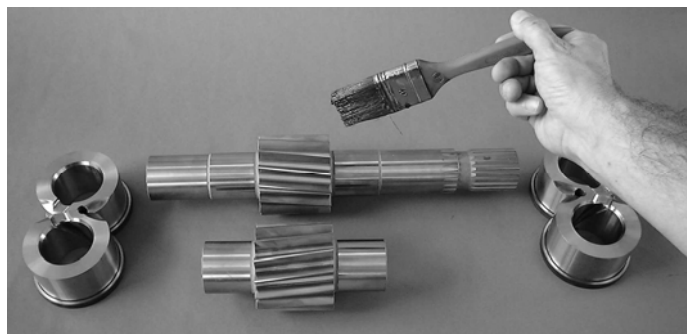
Смазка подшипников скольжения и валов сухой смазочной пленкой
